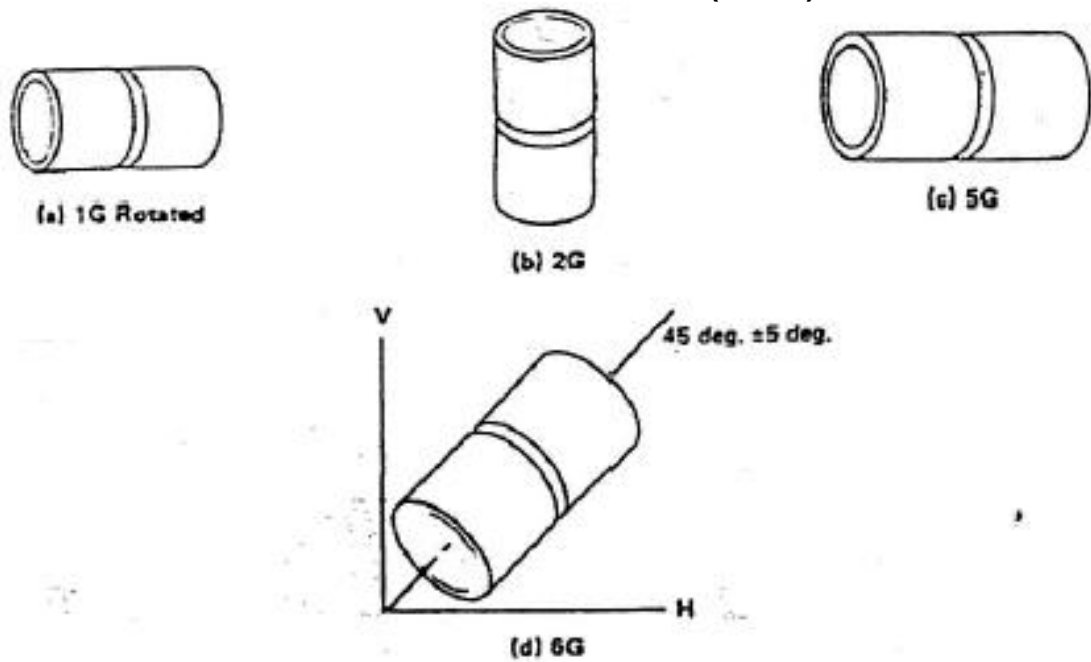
POSICIONES DE SOLDADURA EN TUBO CON SOLDADURA DE RANURA (Ref. 5)
